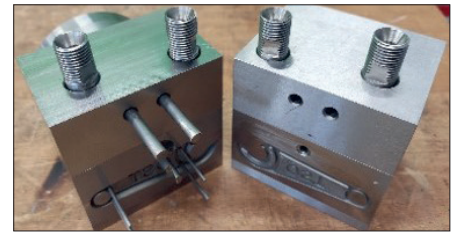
Werkzeug mit montierten Formeinsätzen.
